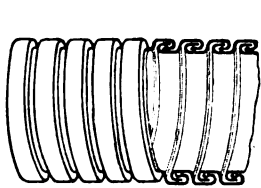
Schlauch mit verfalzten Verbindungen (Hydra-Universalschlauch).
